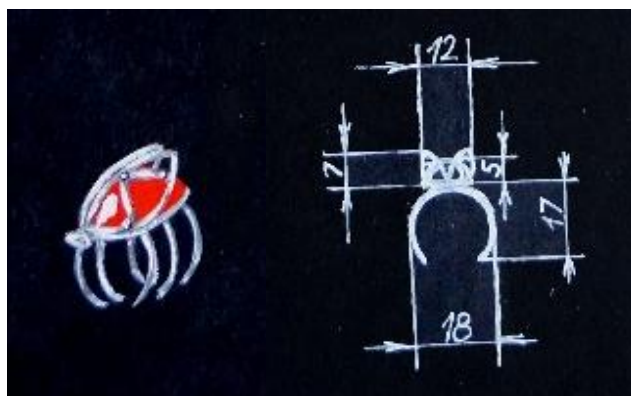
Эскиз и чертеж кольца «Божья коровка»
